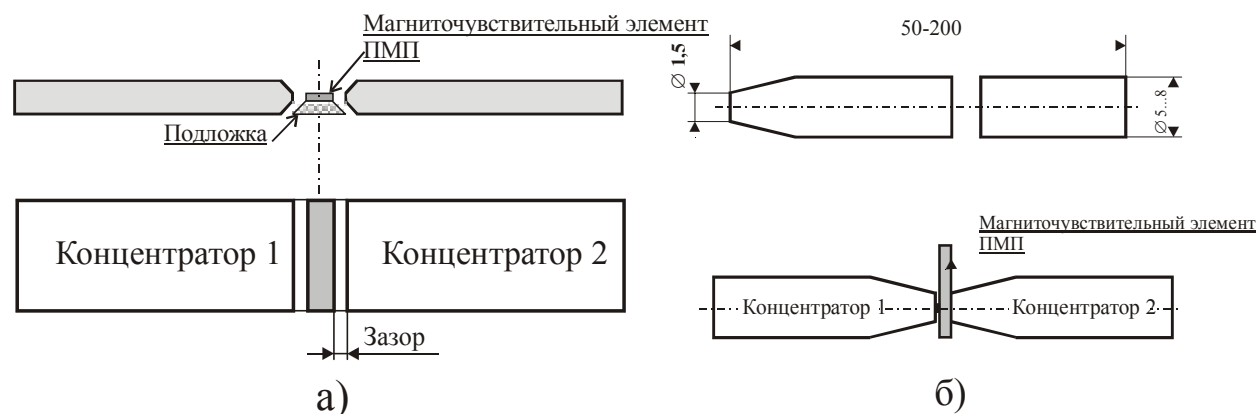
Конструкция цилиндрических концентраторов магнитного поля; а - плоского; б - цилиндрического
